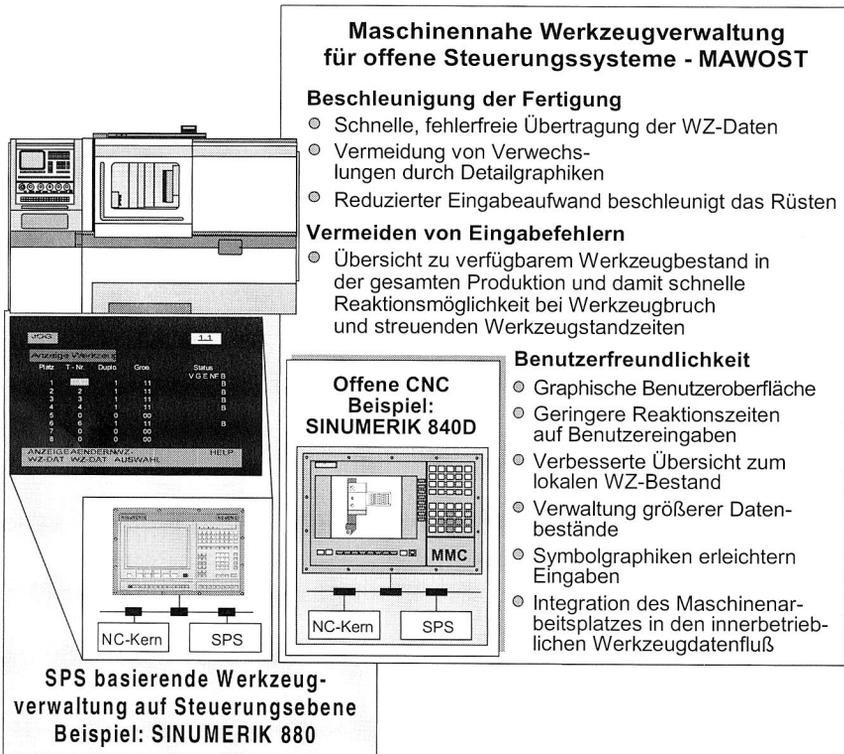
Nutzen einer maschinennahen Werkzeugverwaltung für offene Steuerungssysteme - MAWOST
